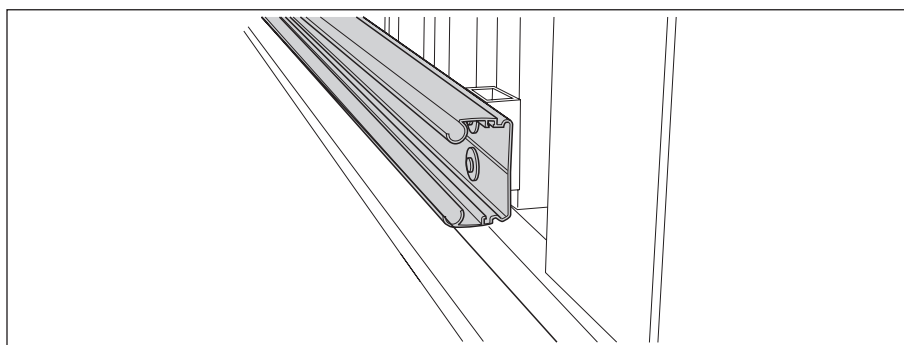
Montaje de la unidad inferior del porta bobinas (ejemplo)
